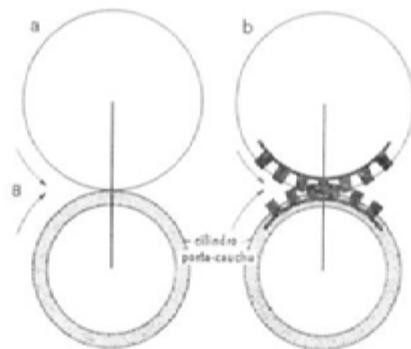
a) Cilindro rígido depois de uma rotação completa em contacto com um cilindro revestido de borracha, com o diâmetro diminuído; b) Os mesmos cilindros com engrenagens depois de uma rotação completa.
